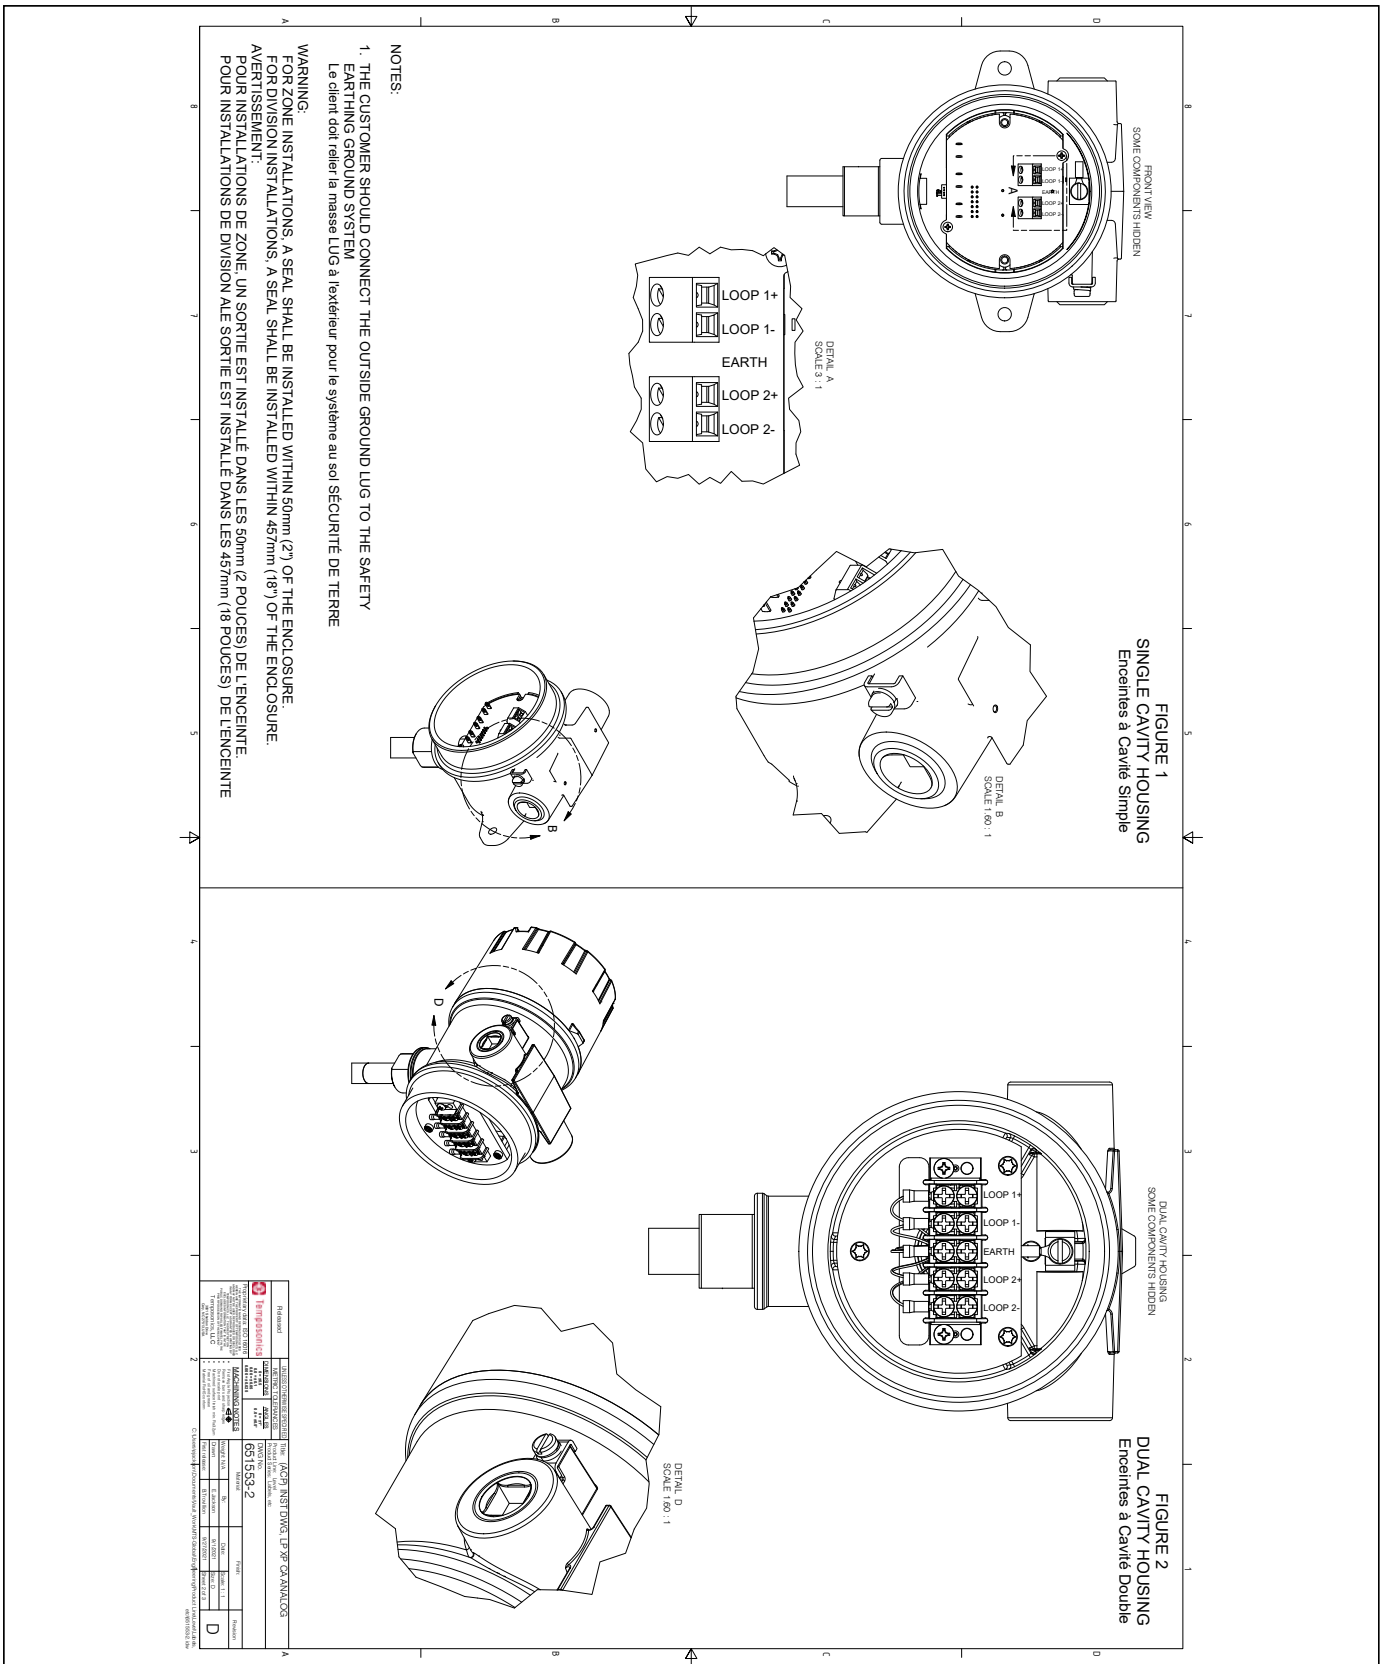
Explosionsgeschützt, FMC-Montagezeichnung, HART®, Seite 2
